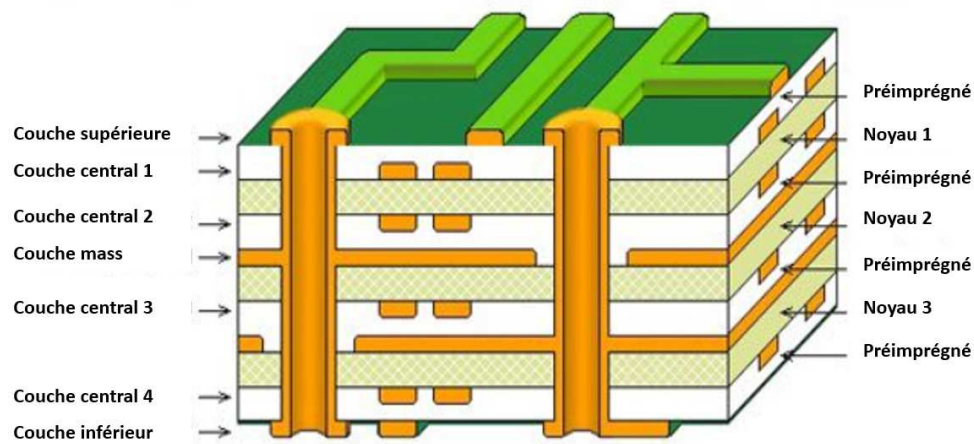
Coupe horizontale d'un PCB à 4 couches
